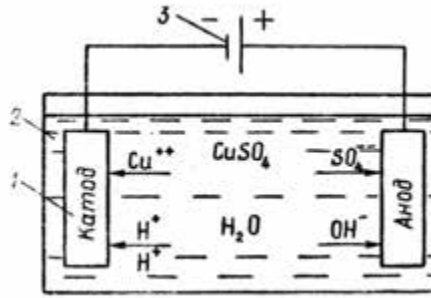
Схема установки для електролітичного осаджування металу:
